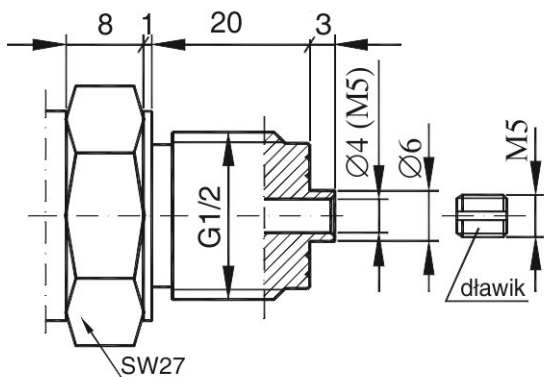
а. Штуцер типа G1/2 с резьбой G1/2"
